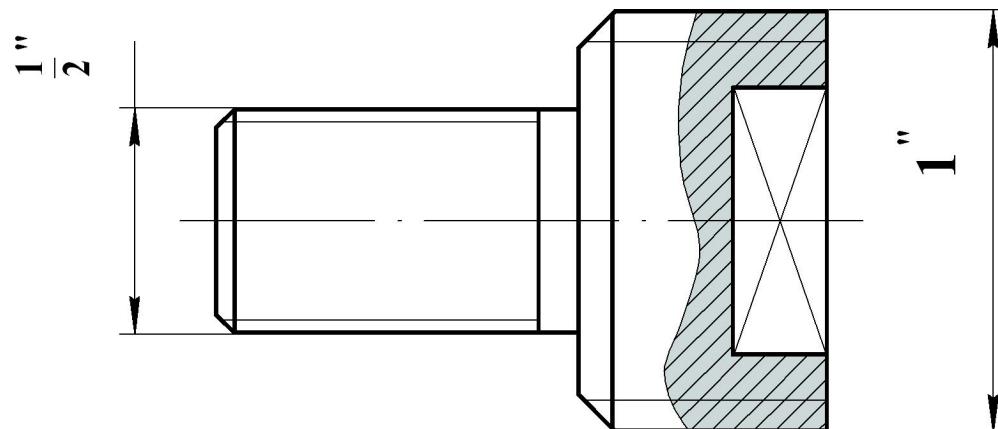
Обозначение цилиндрической дюймовой резьбы
